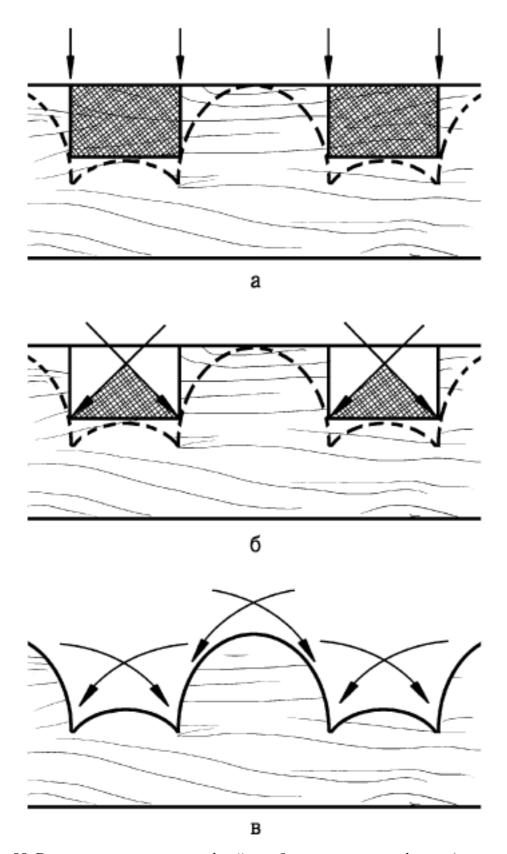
Выполнение плоскорельефной резьбы с подушечным фоном (стрелками показано направление движения инструмента): a — надрезка по контуру рисунка;  $\delta$  — подрезка по направлению к вершине фона;  $\epsilon$  — заоваливание фона и контура рисунка
